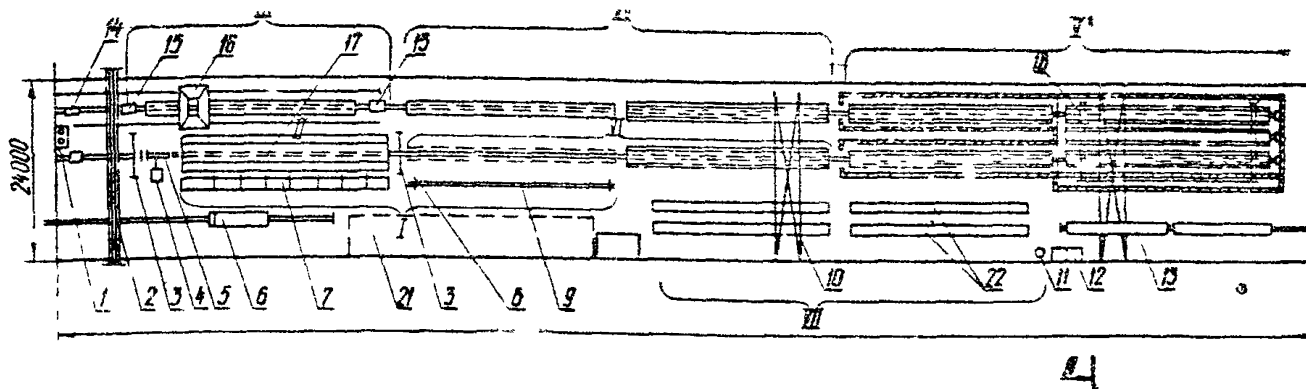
Схема технологической линии: 1 - супергатор для приготовления смазки; 2 - транспортер подачи бетонной смеси; 3 - защитные экраны; 4 - насосная станция; 5 - гидравлический домкрат; 6 - грузонная тележка грузоподъемностью 5 Т; 7 - станець для сборки арматурного каркаса; 8 - опорные стойки; 9 - тросовая для транспортировки арматурного каркаса; 10 - мостовой край; 11 - бетономешалка; 12 - емкость для материалов; 13 - грузовая тележка; 14 - механизм продольного перемещения; 15 - вибропривод; 16 - бетоноукладчик; 17 - передвижной стенд; 18 - механизм поперечной сдвижки; 19 - пульт управления; 20 - тоннельная камера термовлажностной обработки; 21 - площадка для складирования арматуры; 22 - готовый блок
